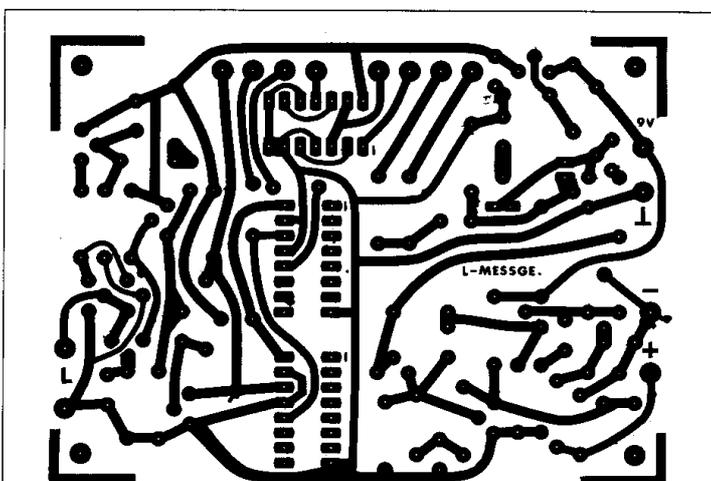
Platinen-Layout zum Aufbau der Schaltung
